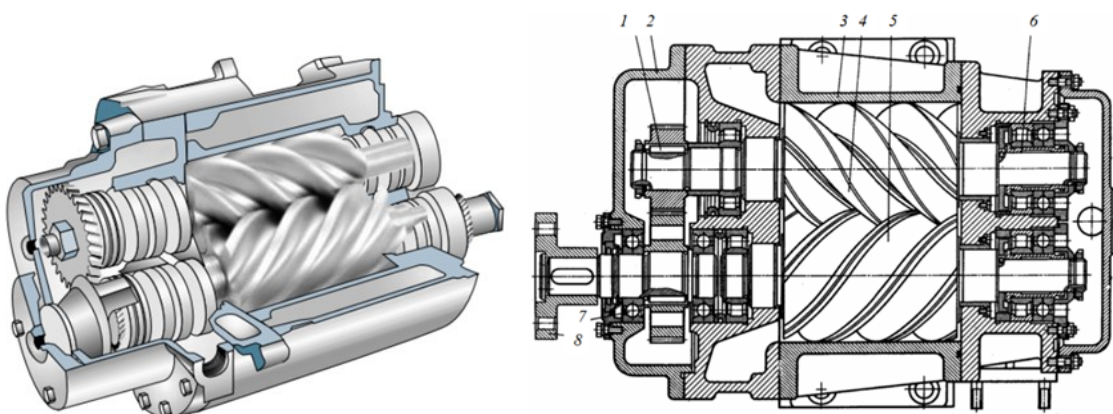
Розріз гвинтового компресора: 1 – редуктор; 2 – кожух; 3 – корпус; 4 – провідний ротор; 5 – ведений ротор; 6, 7 – підшипники; 8 – напівмуфта
